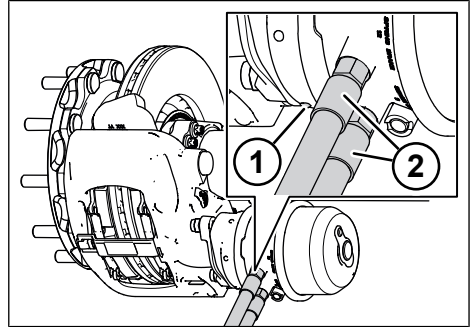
Druckluftleitungen Bremszylinder befestigen
